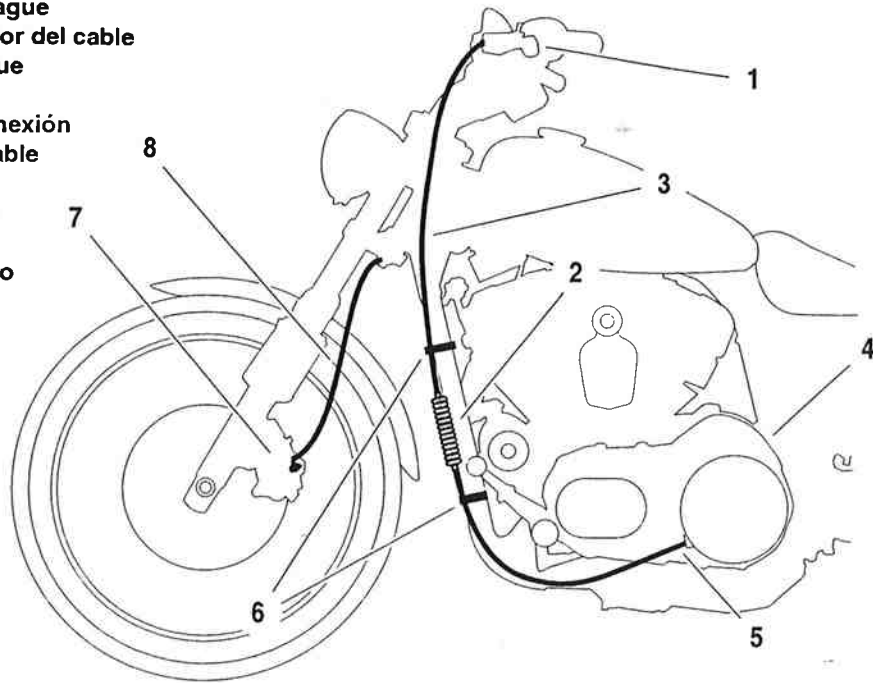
Colocación del cable del embrague y del conducto del freno delantero – lado izquierdo
